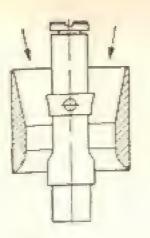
E — A cámara do abaiador (tampa do carburador) pode ser retirada conservando-se o carburador no lugar. Basta que se retirem os parafusos da tampa, como mostra a figura ao lado.
